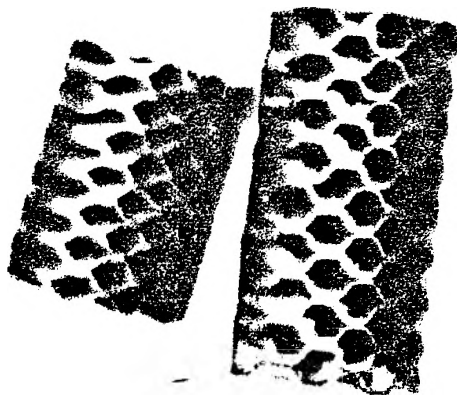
Образцы сотовых конструкций для динамических испытаний
